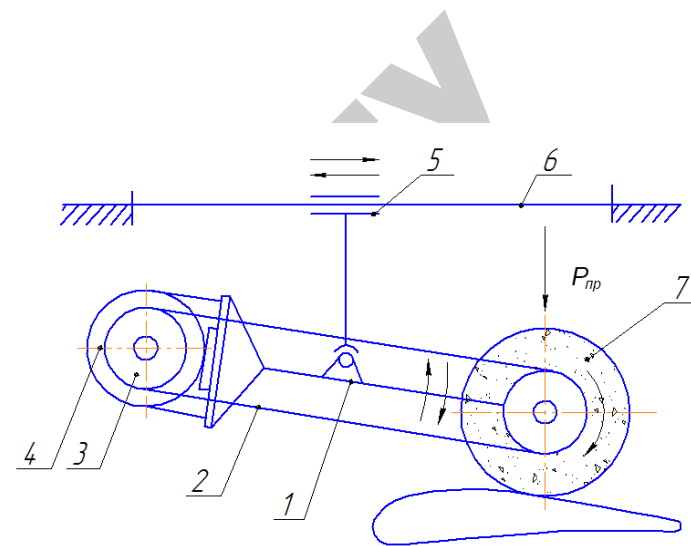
Схема маятниковой шлифовальной головки станка ГФ-259
